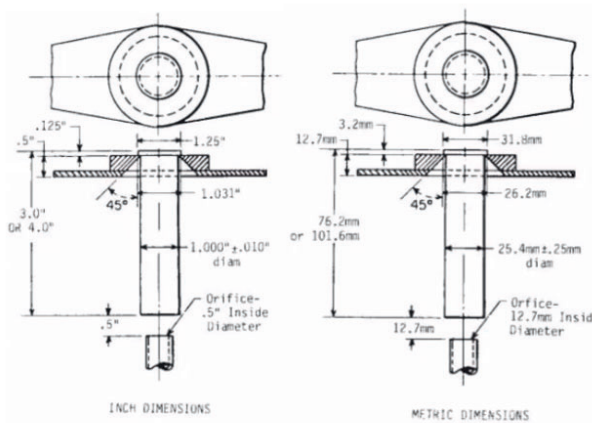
Dimensiones de la probeta para el ensayo Jominy. Fuente: [1]
